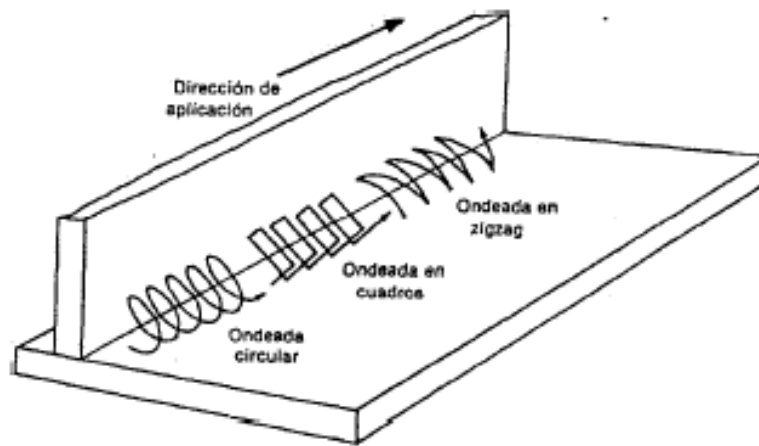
SOLDADURA ONDEADA (Ref. 4)
